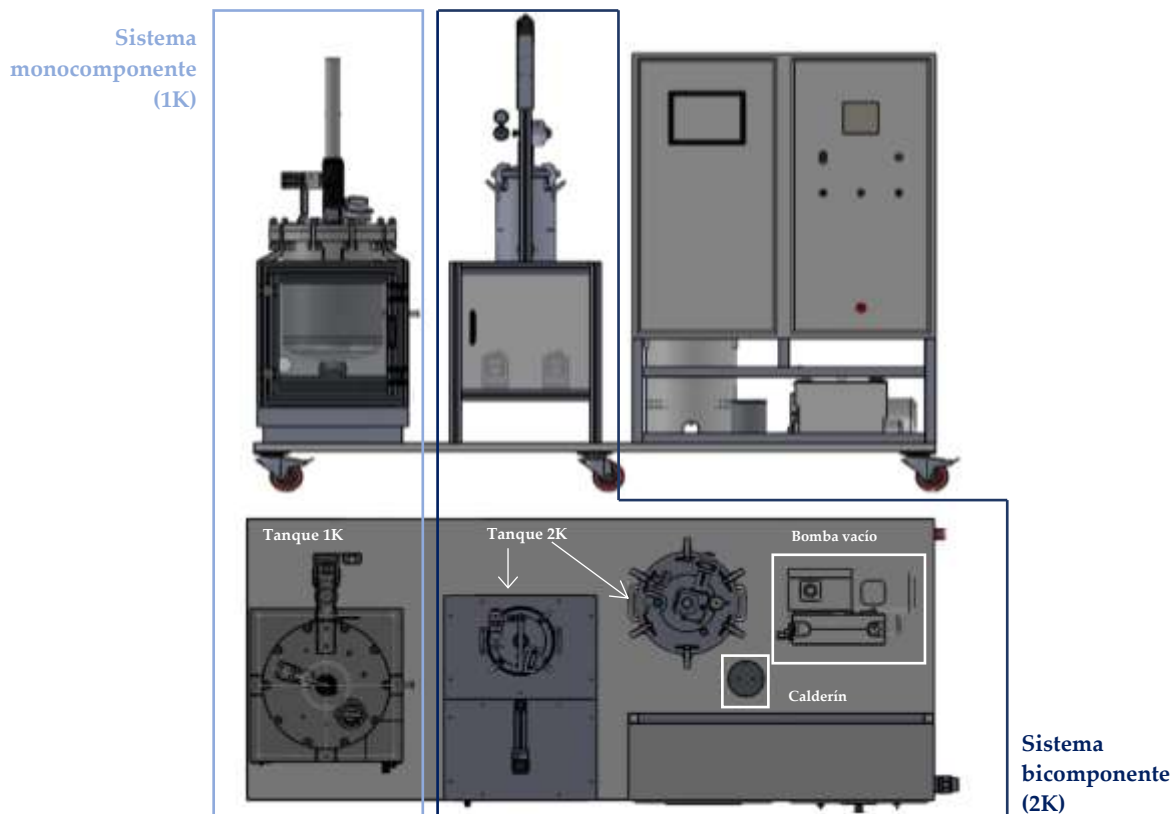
Vistas de alzado y planta del equipo de inyección, divididas en el sistema monocomponente (1K), bicomponente (2K) y de vacío.
